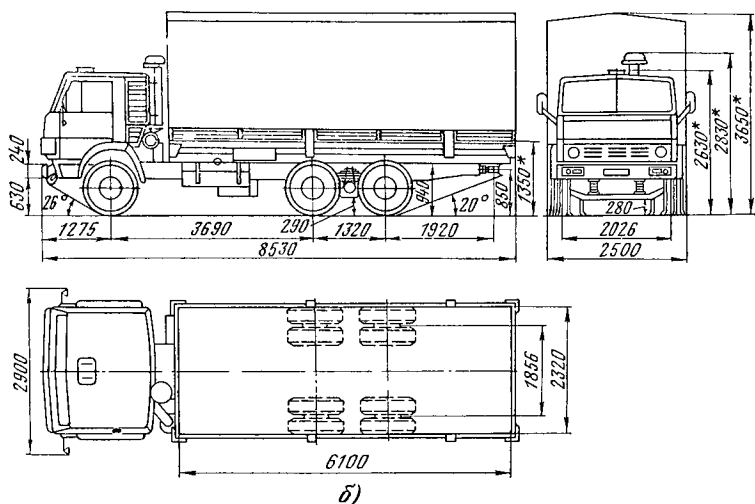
б — автомобиля-тягача КамАЗ-53212 (размеры даны для автомобиля полной массы, размеры со звездочкой — для снаряженного автомобиля)
